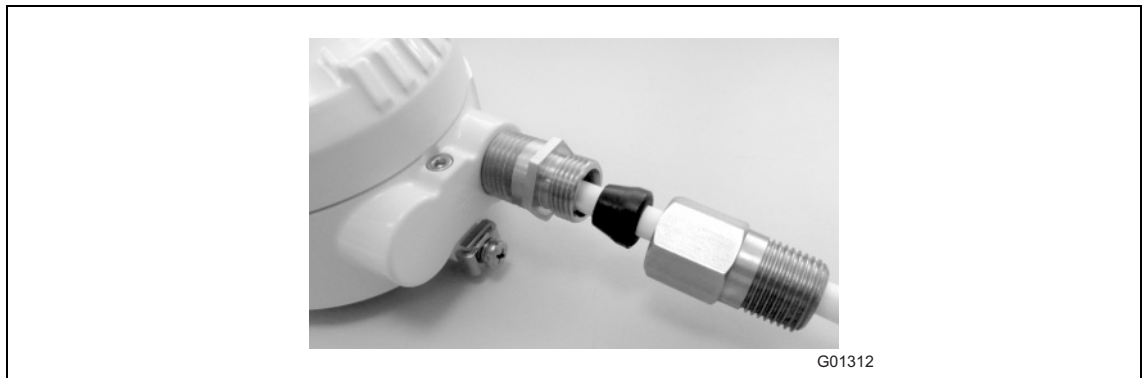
Kit di montaggio per il tubo di protezione dei cavi
